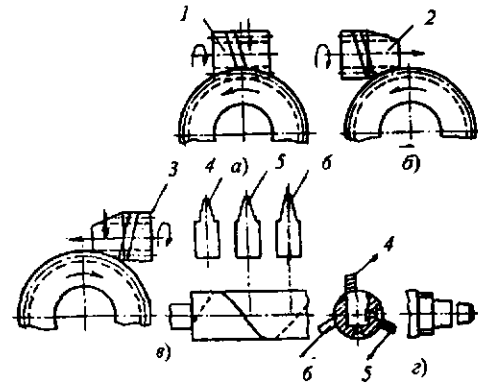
Схемы методов нарезания зубьев червячного колеса
